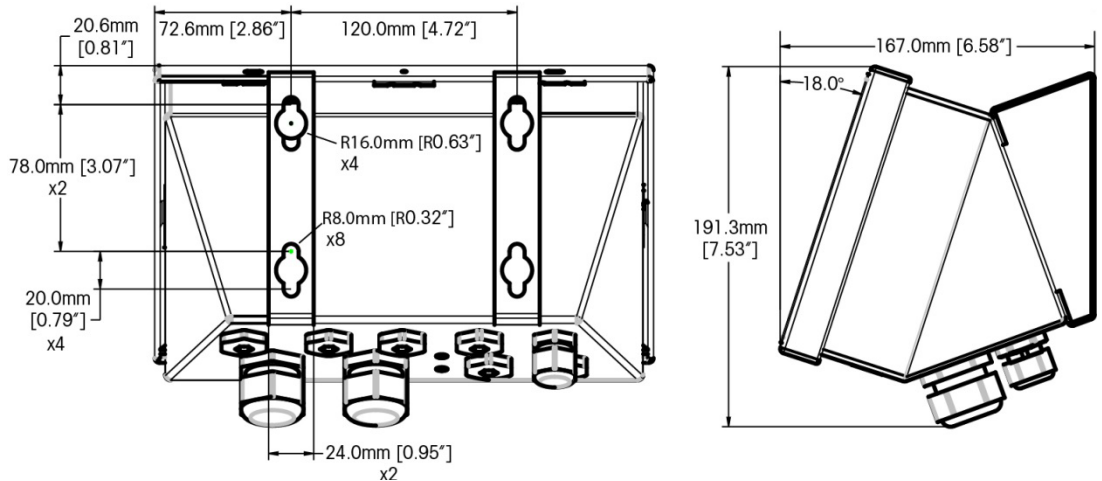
Dimensões do gabinete para ambiente adverso IND570xx com suportes de montagem de ângulo fixo, originais padrão de montagem
